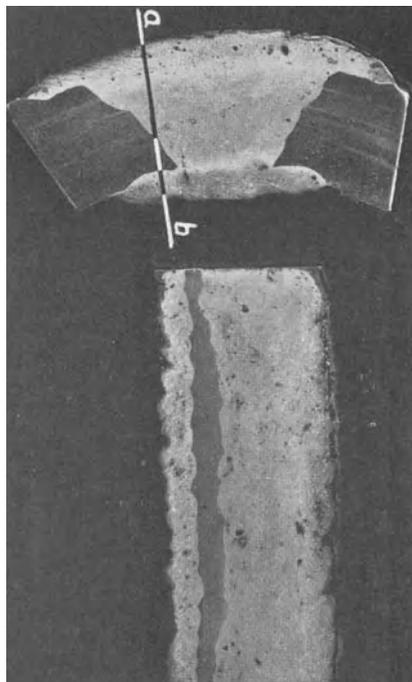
Schweißnaht eines Wasserrohrs in einem Torpedobootskessel.
